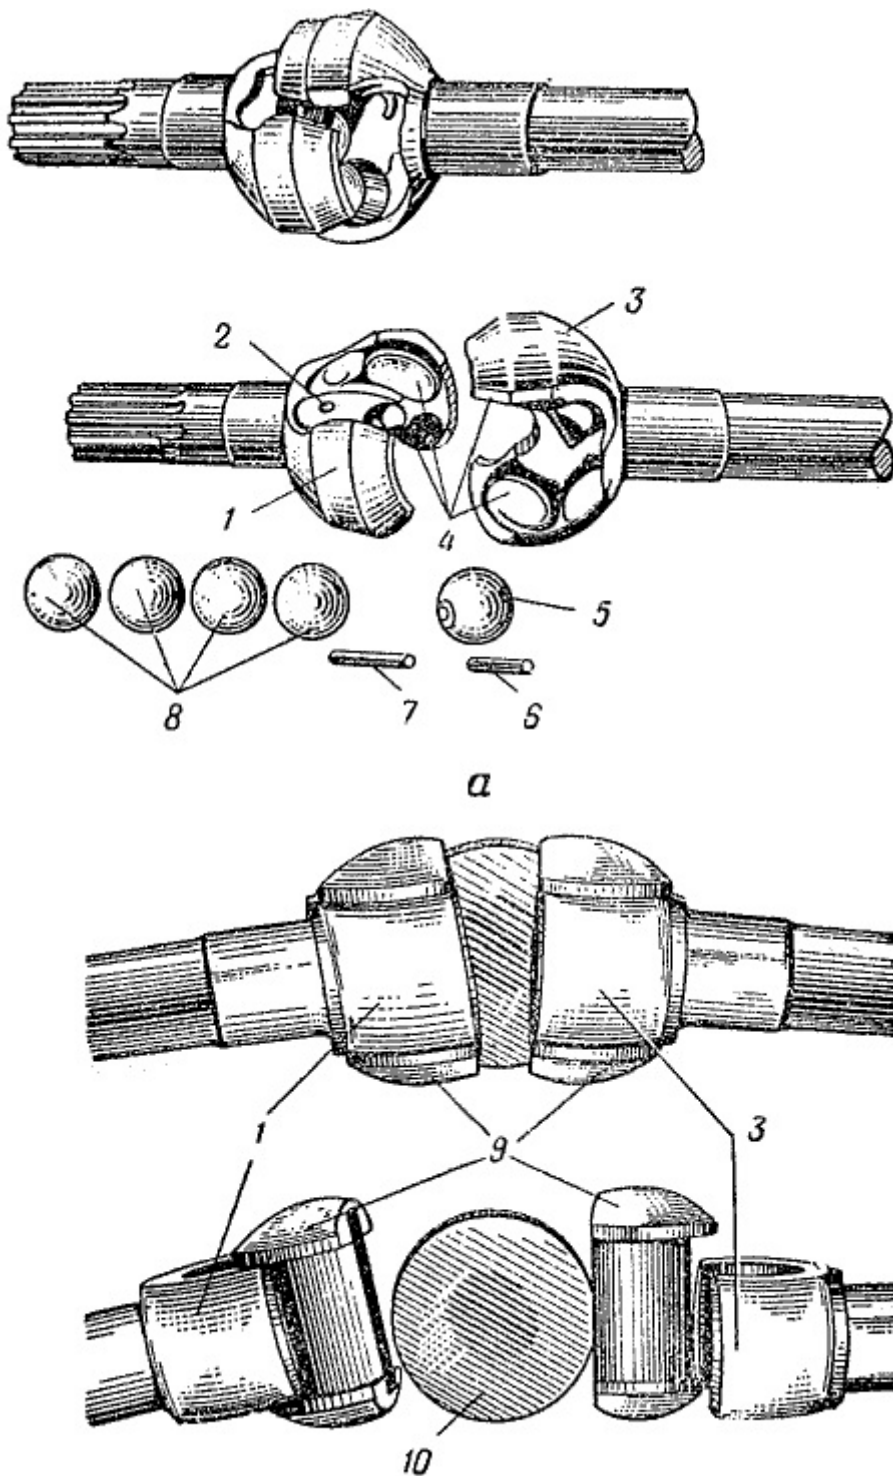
Шарниры равной угловой скорости: а — шарикового типа; б — дискового типа; 1 — вилка полуоси колеса; 2 — отверстие для шпильки; 3 — вилка полуоси; 4 — фигурные канавки; 5 — центральный шарик; 6 — шпилька; 7 — палец; 8 — шарики; 9 — кулаки; 10 — диск
